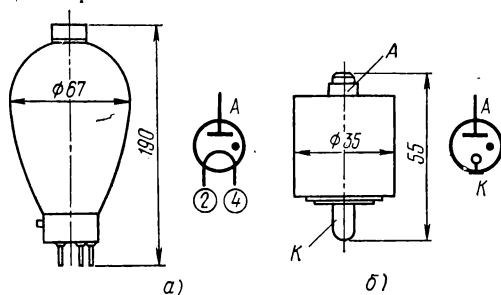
Габаритные чертежи и цоколевка газотронов:
